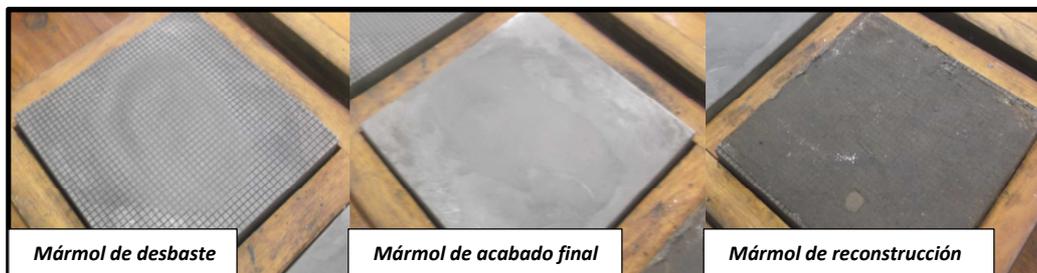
Mármol de desbaste, Acabado final y reconstrucción de planos.
